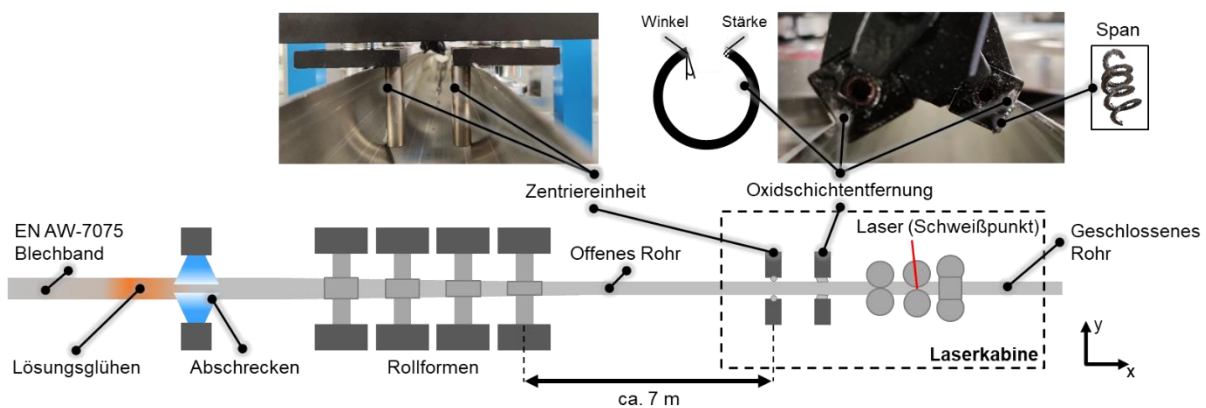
Draufsicht auf die Prozesskette zur Inline-WBH, zum Rollformen und zum Schweißen des hochfesten Aluminiumrohrs. Detailansicht der Zentriereinheit und der Oxidschichtentfernung.
